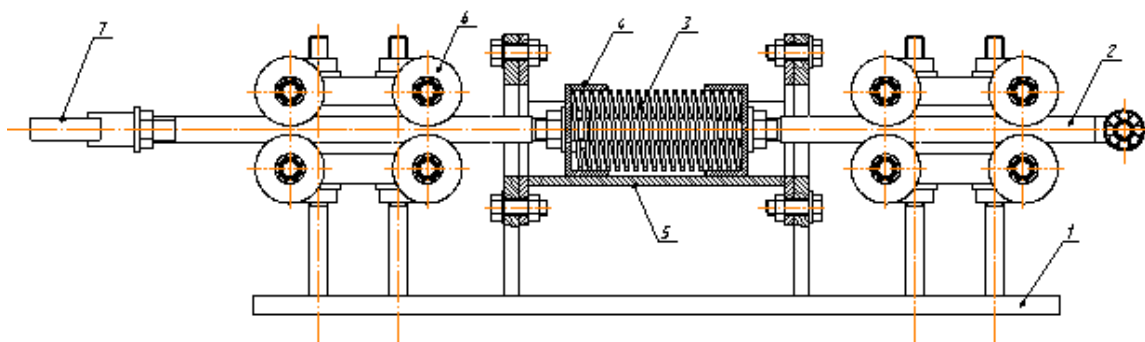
Схема расположения пружины в цилиндре и расположение штоков в роликах: 1 - основание; 2 - шток; 3 - пружина; 4 - стакан; 5 - цилиндр; 6 - ролик; 7 - штуцер
